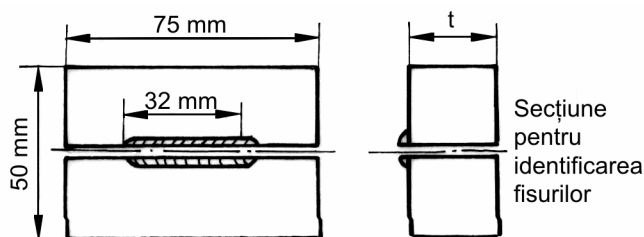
Dimensiunile epruvetelor pentru probe tip Jackson
